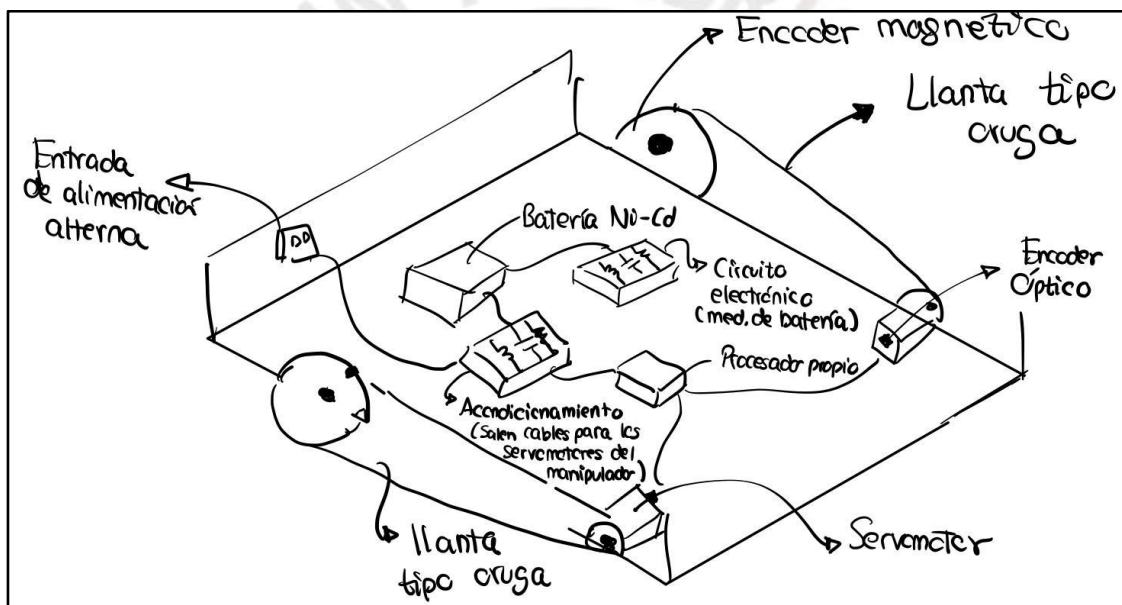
Vista interior de cubierta metálica - Concepto de solución 3. Elaboración propia.
